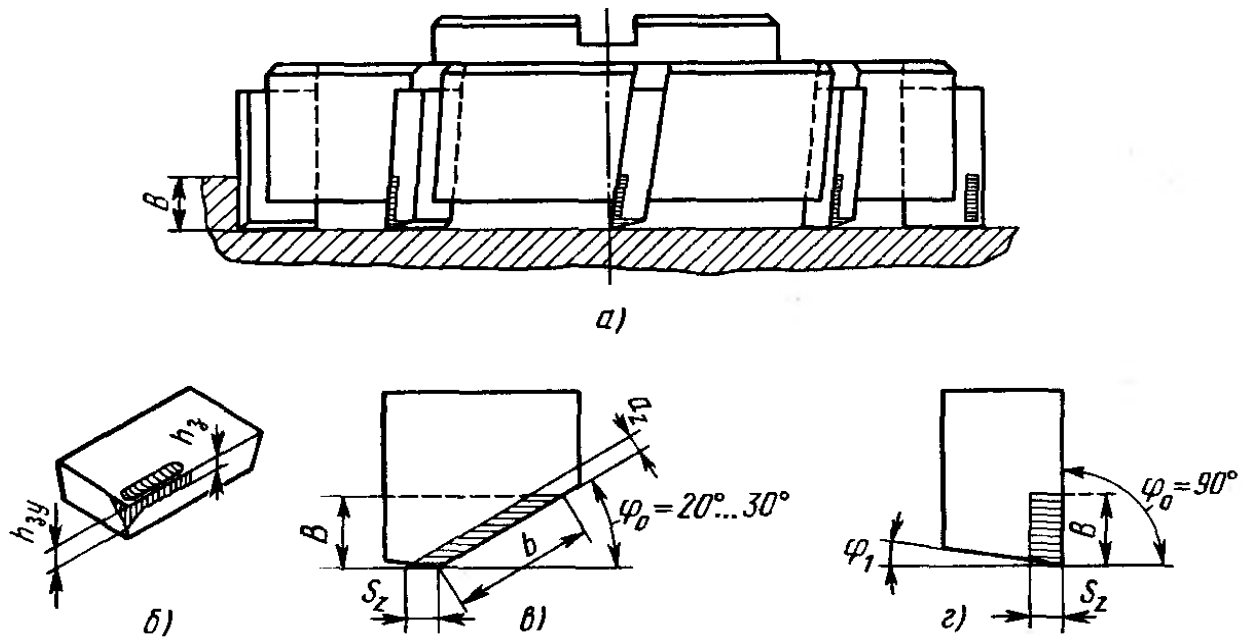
Рис 2.11. Схема зношення лез ножів торцьової фрези
